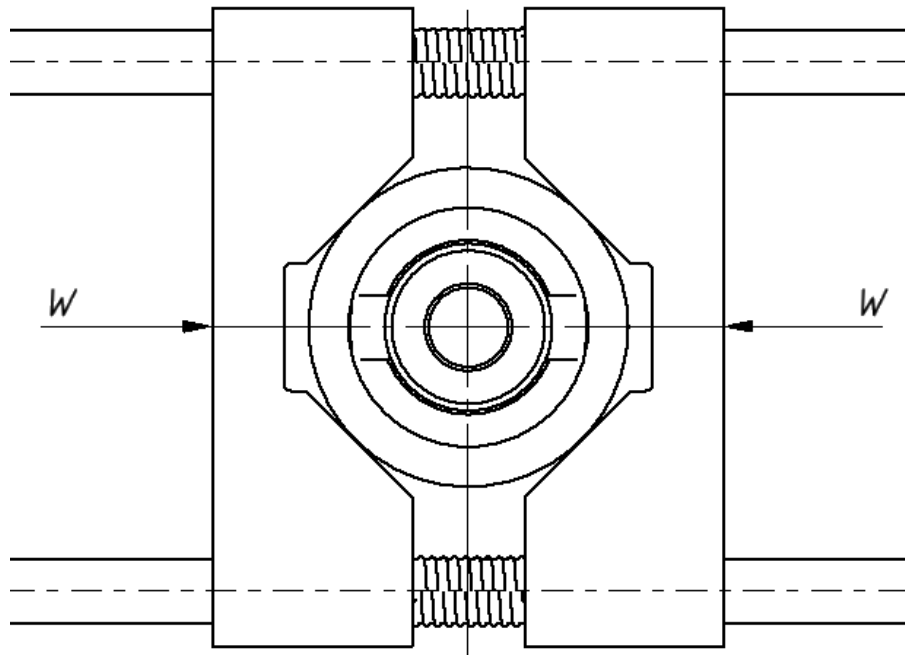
Схема затиску деталі для обробки [24]
